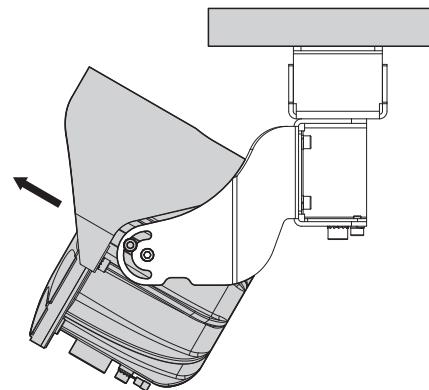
Installazione a soffitto (rotazione verticale, +30°).
